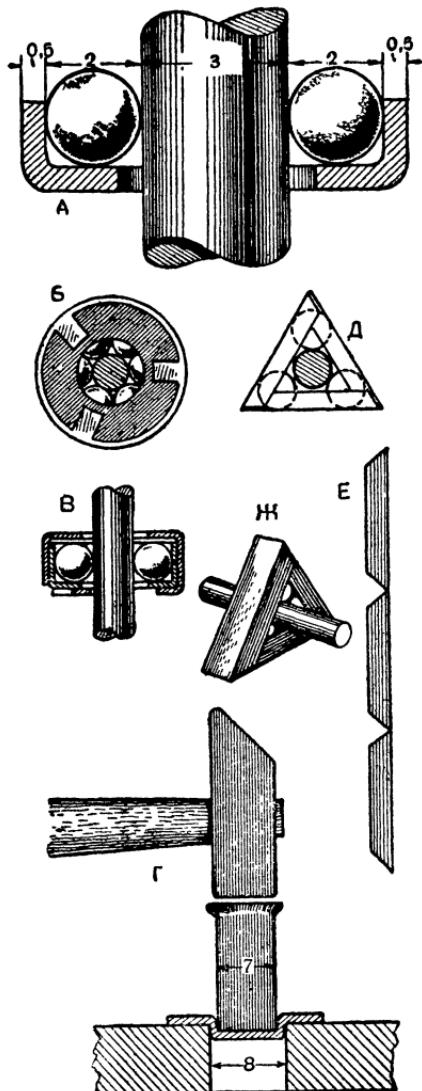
Самодельные шарикоподшипники. Первый вариант: А — схема размеров; Б — вид собранного подшипника сверху; В — собранный подшипник в разрезе; Г — прием изготовления чашки. Второй вариант: Д — схема подшипника; Е — заготовка обоймы (вид сбоку); Ж — собранный подшипник.
